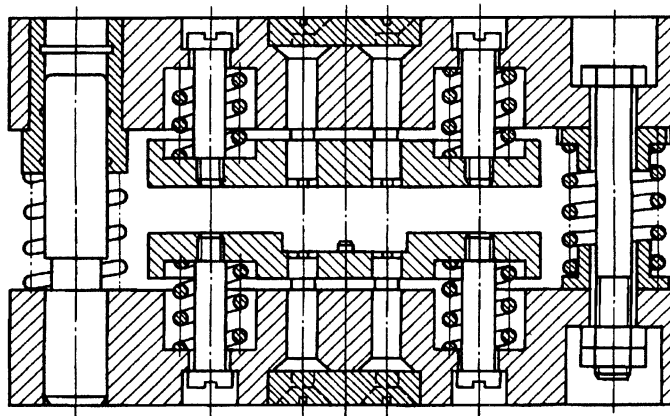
Типовой штамп для точечной холодной сварки
